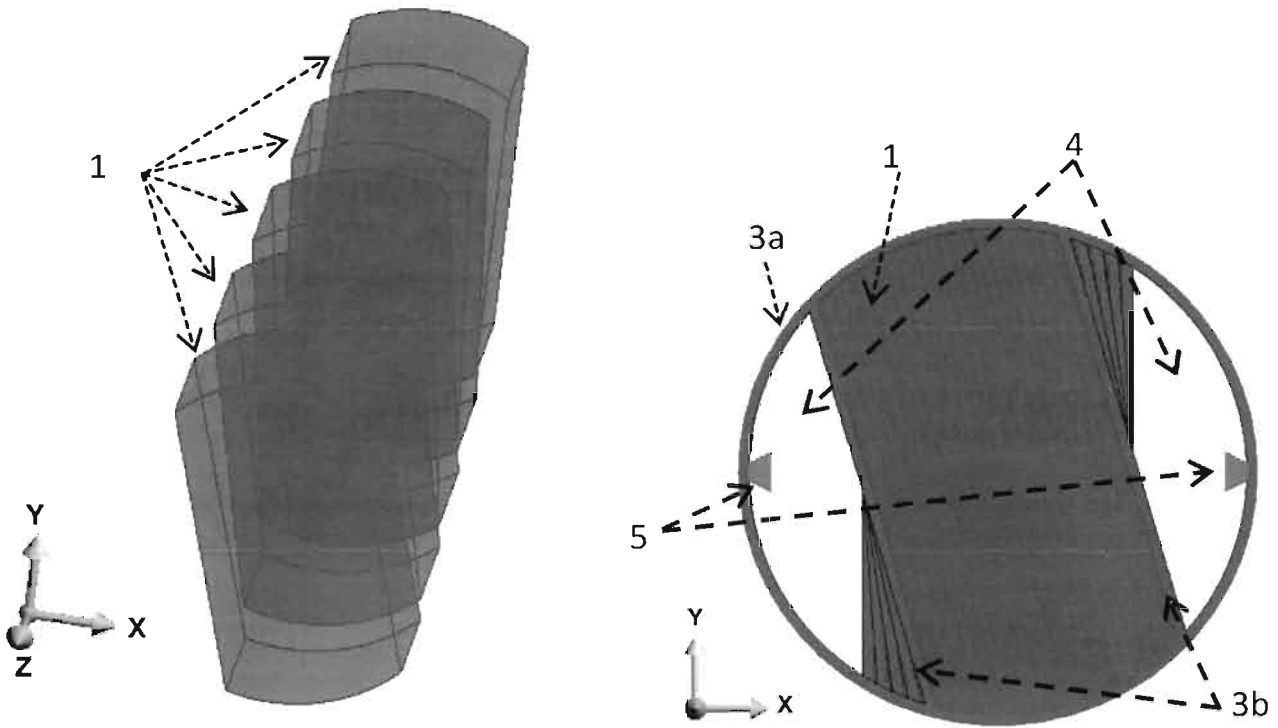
Vedere 3D a rotorului MSR cu rotor modular cu unghi de decalaj de dentaură (stânga) și vedere 2D cu rotorul cu tole axiale și tubul nemagnetic de consolidare (dreapta).
